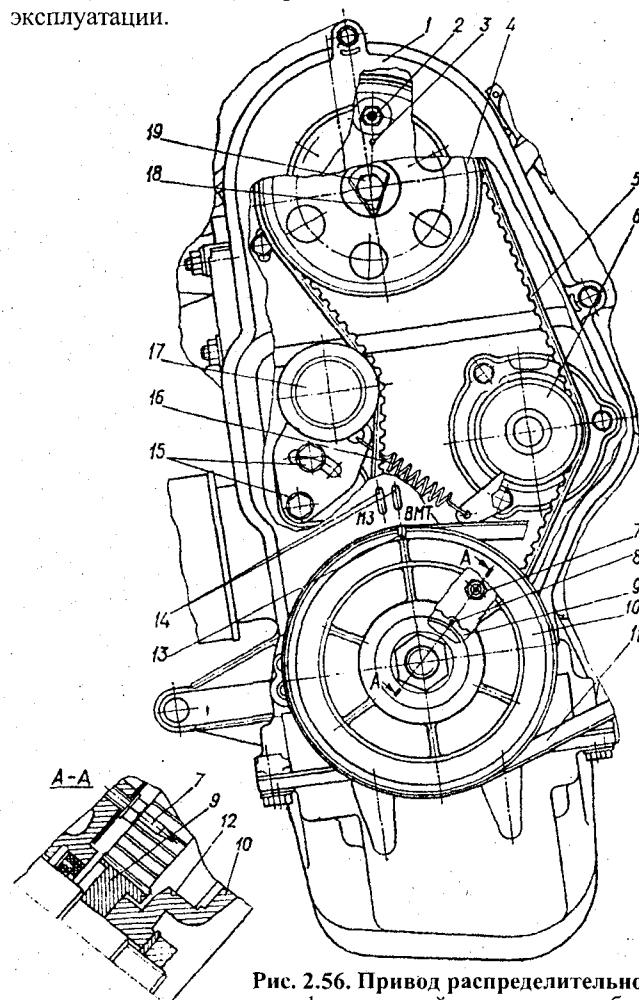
Привод распределительного ремня: 1 — наружный кожух плоскозубчатого ремня; 2 — стрелка установки ведомого шкива распределительного вала; 3 — метка на шкиве распределительного вала; 4 — ведомый шкив распределительного вала; 5 — плоскозубчатый ремень; 6 — шкив водяного насоса; 7 — стрелка установки ведущего шкива привода распределительного вала в ВМТ; 8 — метка ВМТ на ведущем шкиве; 9 — ведущий шкив привода распределительного вала; 10 — шкив привода генератора; 11 — ремень привода генератора; 12 — метка ВМТ (сверленное гнездо диаметром 4 мм) на ступице шкива привода генератора; 13 — метка ВМТ на шкиве привода генератора (прорез на наружной стороне шкива); 14 — метки ВМТ и МЗ на верхнем кожухе зубчатого ремня; 15 — болты кронштейна натяжного ролика; 16 — пружина натяжного ролика; 17 — натяжной ролик; 18 — отгибная шайба; 19 — болт крепления шкива
